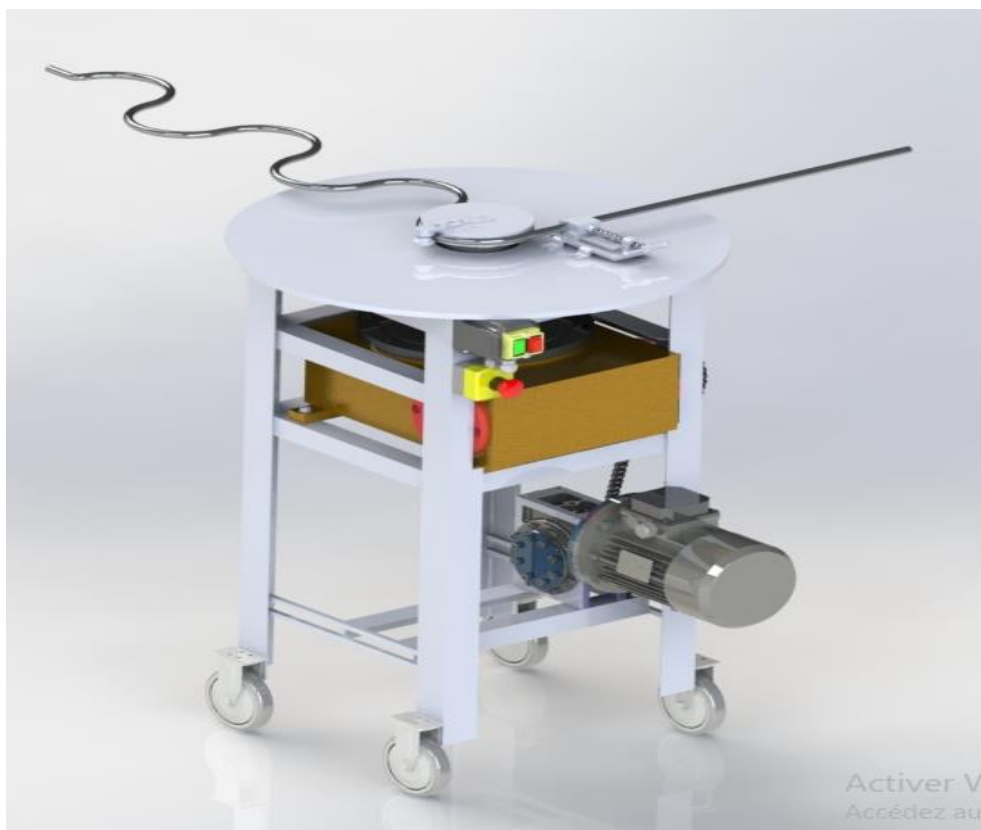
(c): Dessin d'assemblage de la cintreuse plane
